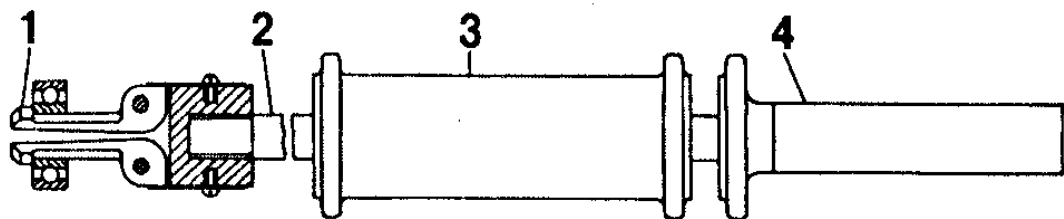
Съемник 7823-6090 для выпрессовки подшипника первичного вала коробки передач из коленчатого вала:
